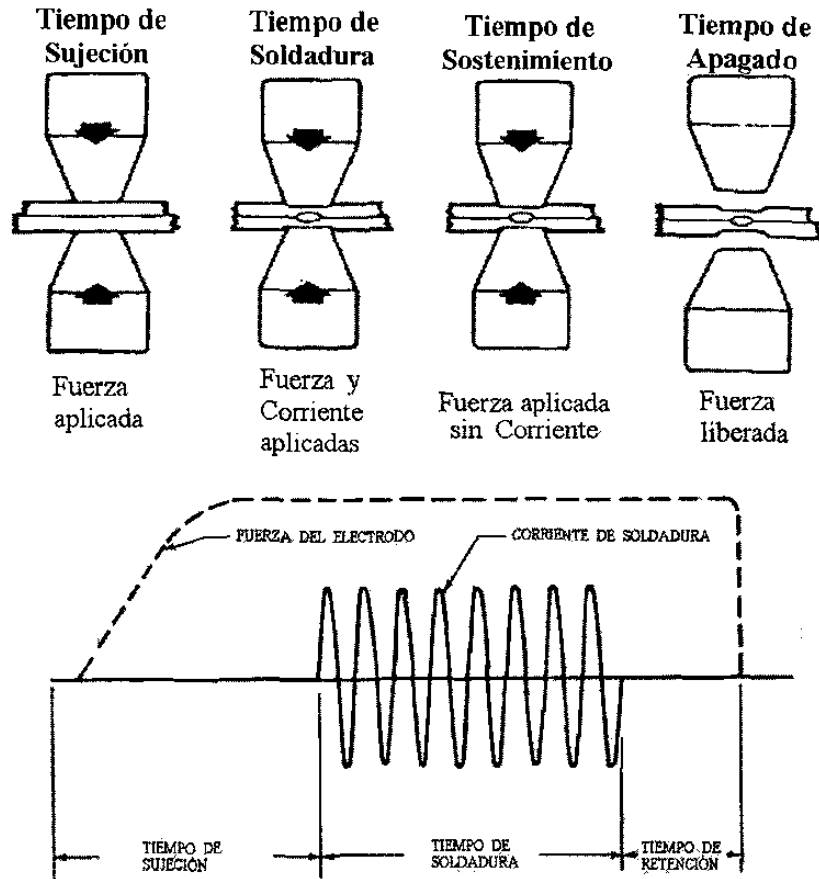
Ciclo típico del proceso de soldadura por puntos⁽⁴⁸⁾.
